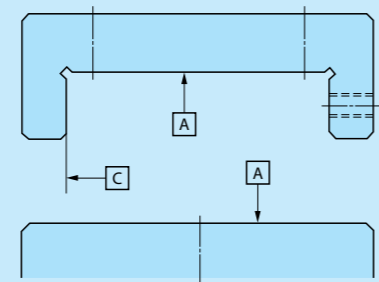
Bearbeitungsbeispiel Montagefläche von CRWM
